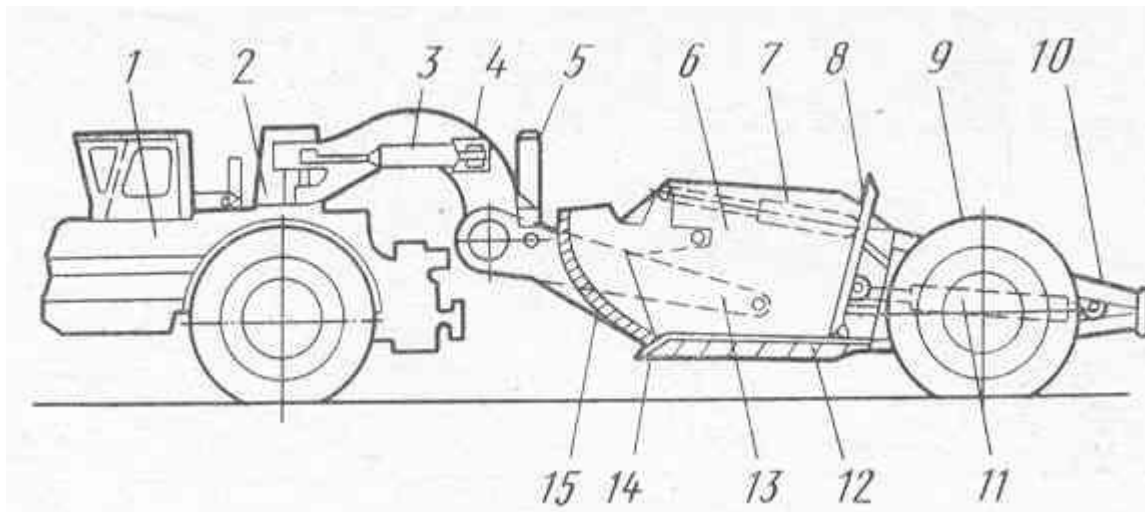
1 – одноосный тягач; 2 – седельно–цепное устройство; 3 – гидроцилиндр поворота; 4 – дышло (арка–хобот); 5 – гидроцилиндр подъема ковша; 6 – ковш; 7 – гидроцилиндр заслонки; 8 – задняя подвижная стенка; 9 – заднее колесо; 10 – буфер для толкача; 11 – гидроцилиндр выдвижения задней стенки; 12 – днище ковша; 13 – тяговая рама; 14 – нож; 15 – передняя заслонка.
